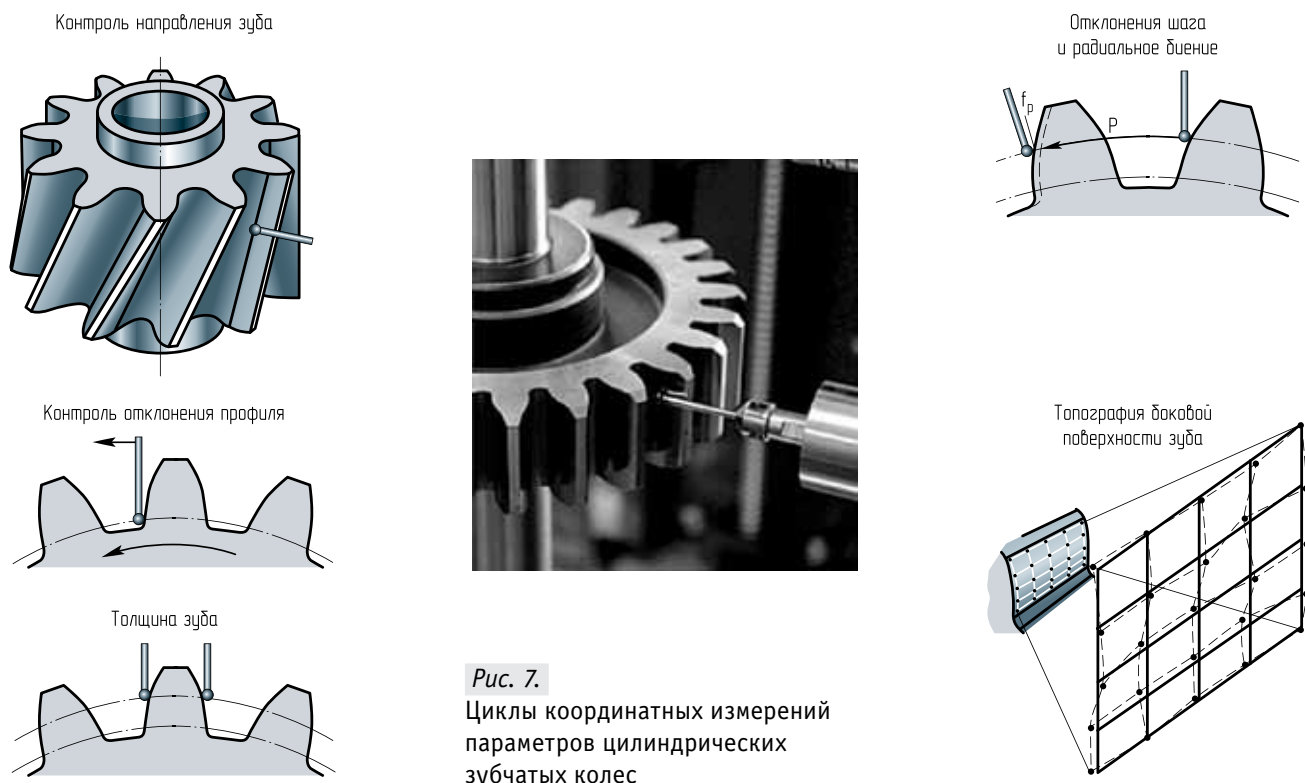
Циклы координатных измерений параметров цилиндрических зубчатых колес
